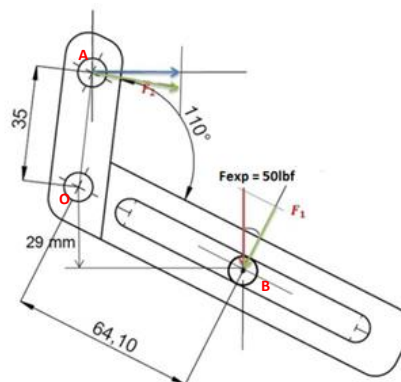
Fuerza de cierre del molde encontrada experimentalmente
